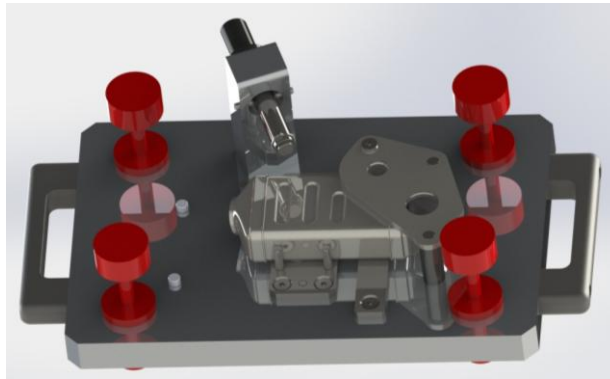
Utillaje de soldadura láser de fase 3. Posición de soldeo de brida de entrada de gases.
